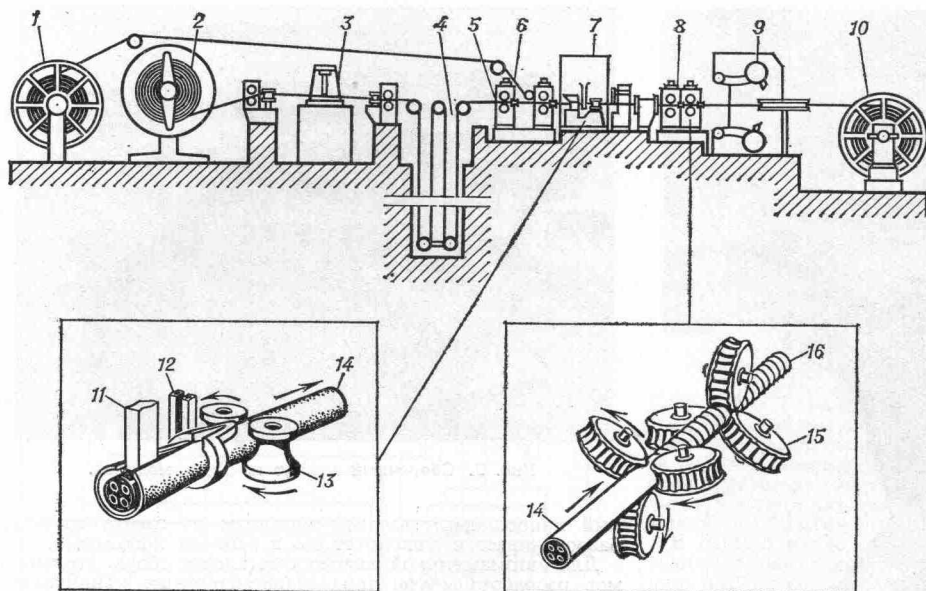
Схема агрегата для ВЧ сварки алюминиевых и стальных кабельных оболочек.
